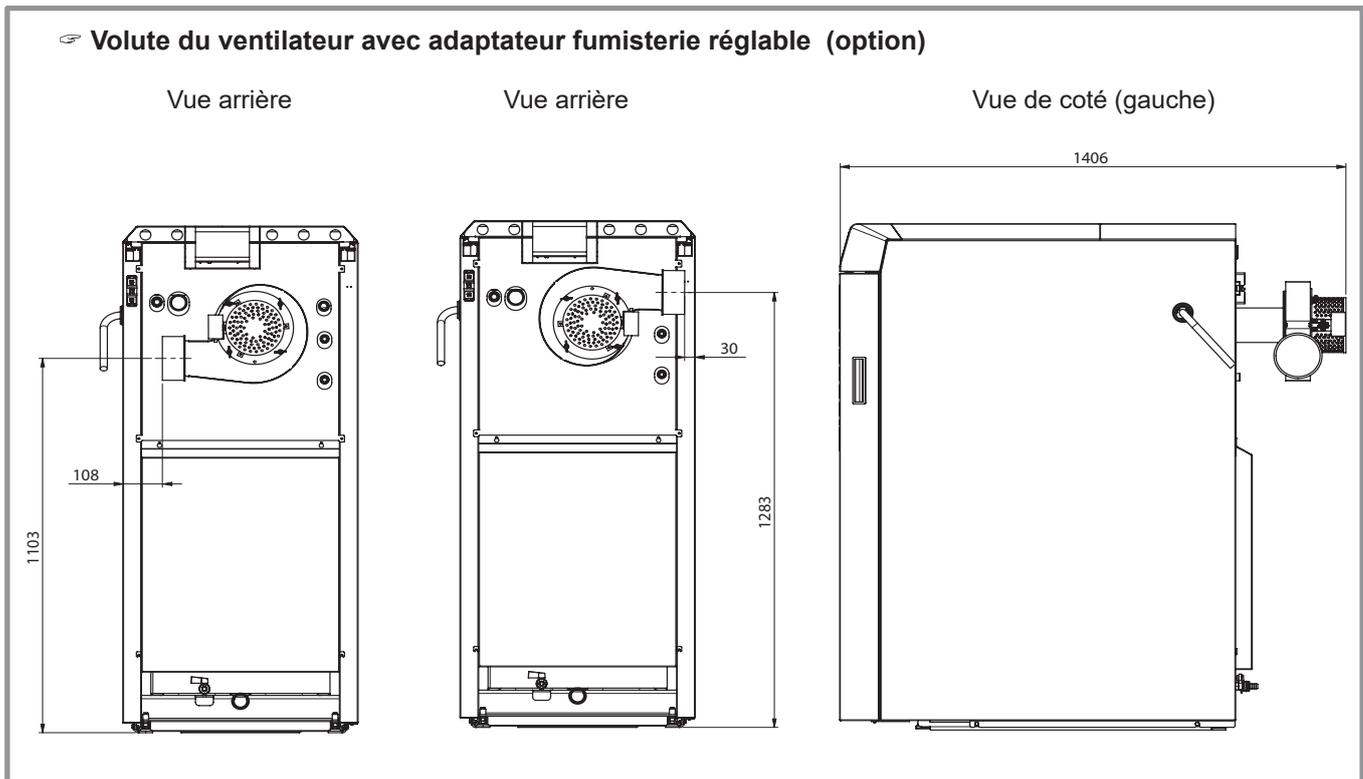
Ventilateur monté avec adaptateur sur la chaudière (dimensions en mm)
